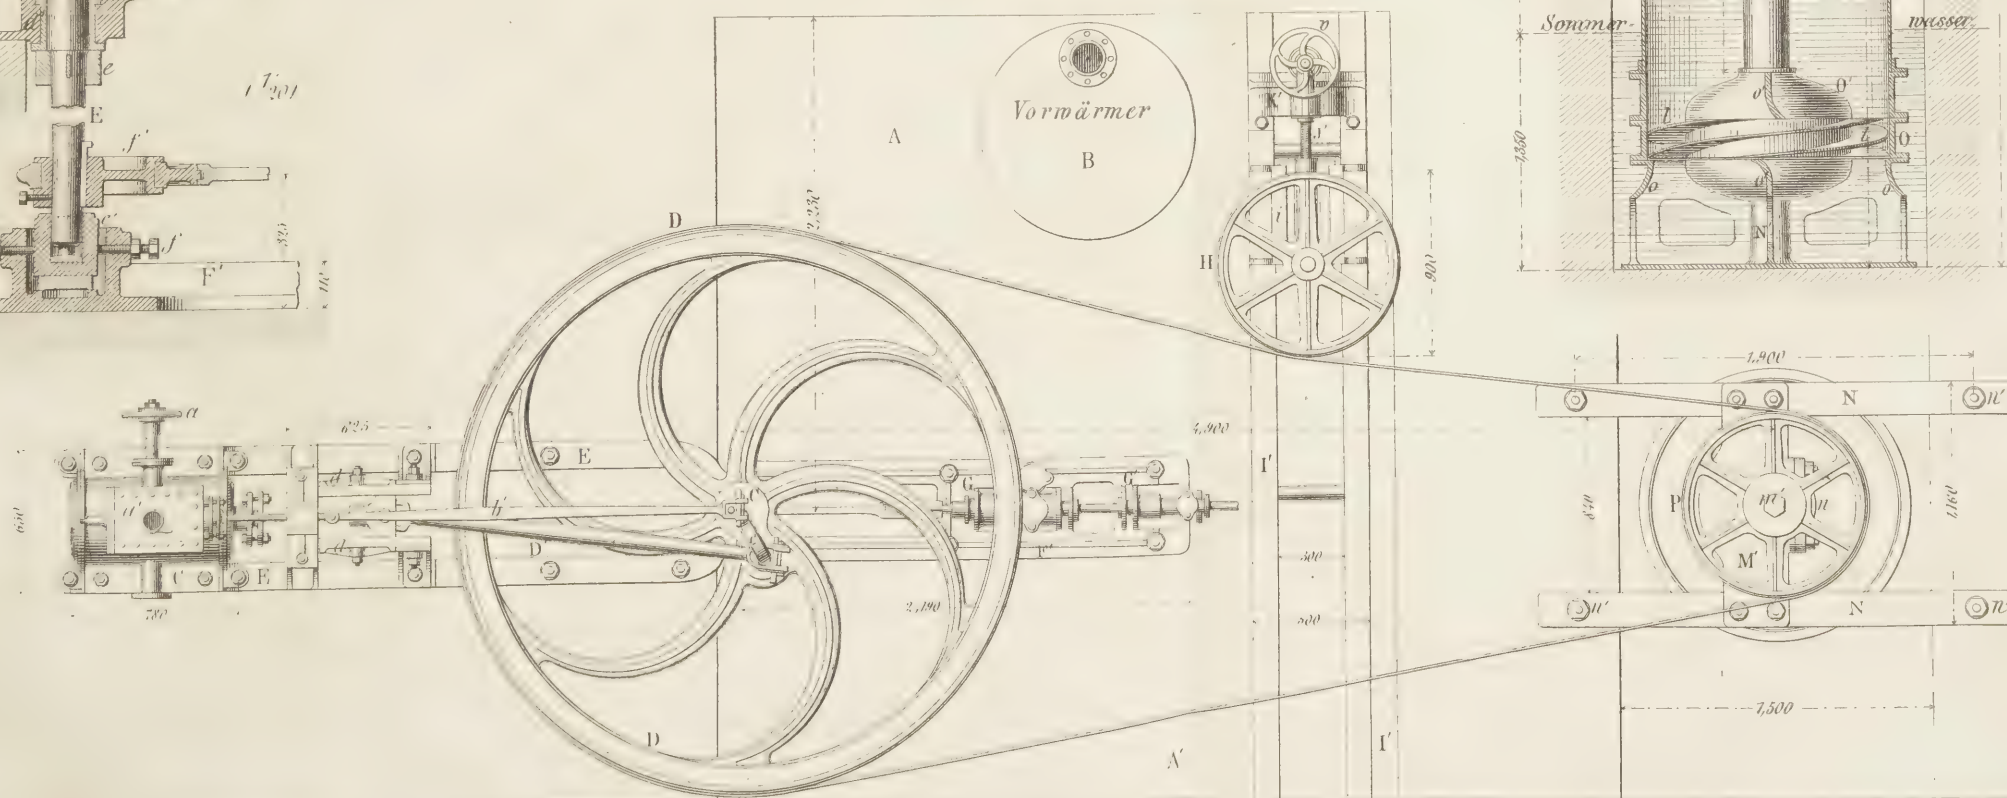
Grundriss der Anlage. (1/40)
